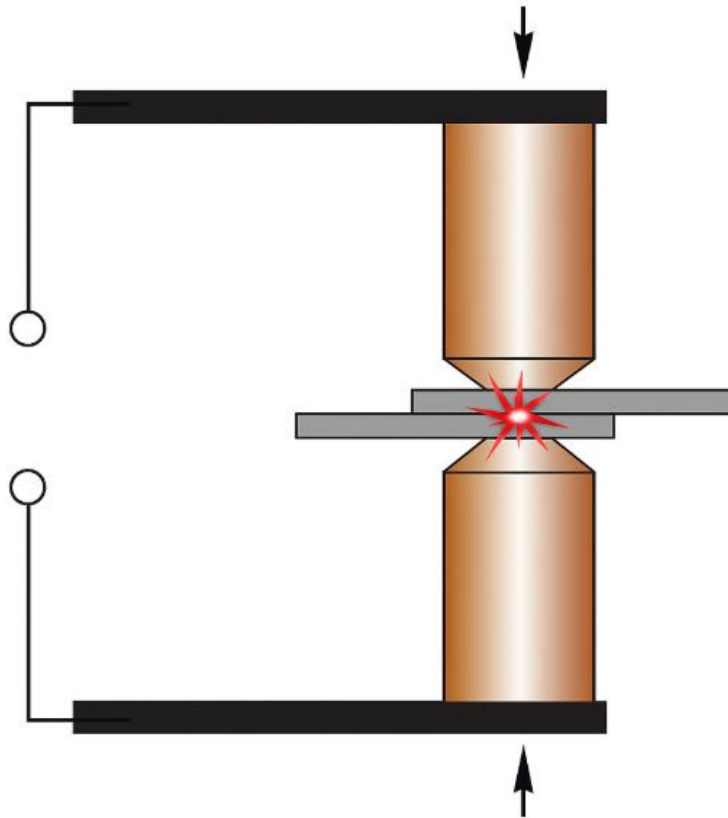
Схема контактної точкової зварювання [5]
